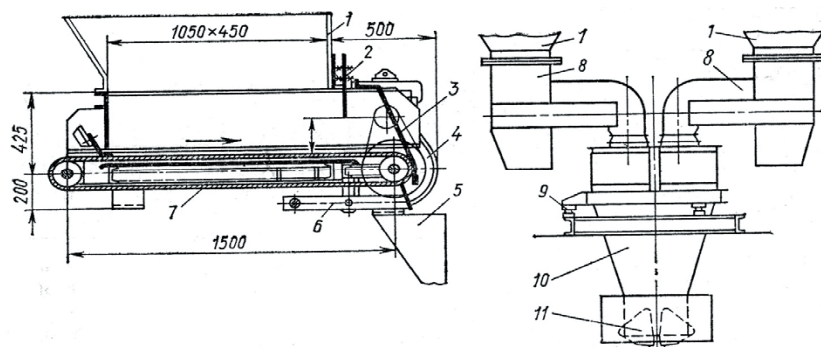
Устройства для дозирования сыпучих компонентов смесей: а – ленточный объемный дозатор; б – бункерный весовой дозатор; 1 – бункер для готовой смеси; 2 – регулирующий шибер; 3 – штора; 4 – привод; 5 – лоток для смеси; 6 – скребок; 7 – ленточный конвейер; 8 – ленточный питатель; 9 – тензодатчики; 10 – весовая емкость; 11 – челюстной затвор с пневмоприводом
